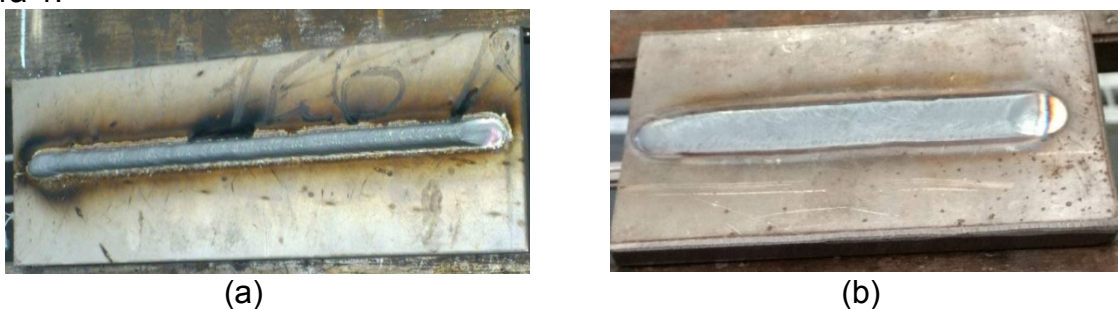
Exemplo da deposição de cordão de solda sobre a chapa utilizando (a) o processo MIG, (b) o processo TIG.
